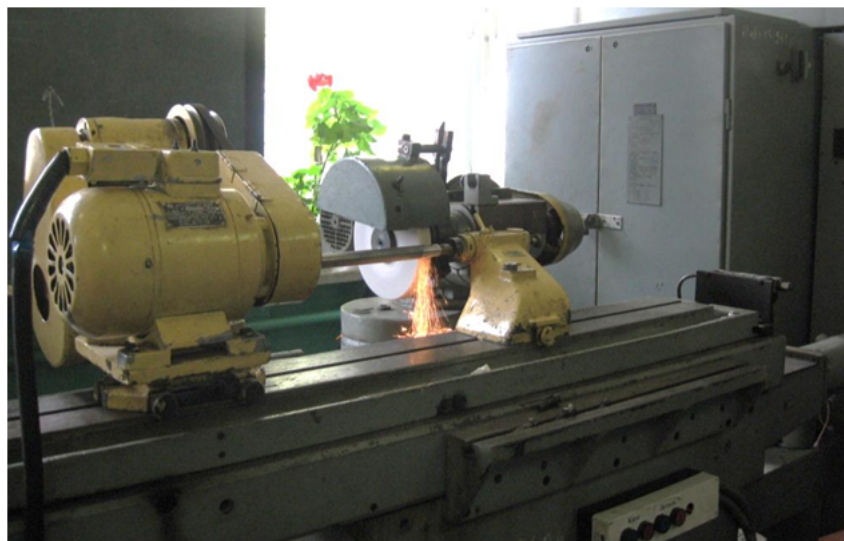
Шліфування циліндричного вала зі схрещеними осями абразивного круга та деталі на верстаті моделі В3208Ф3
